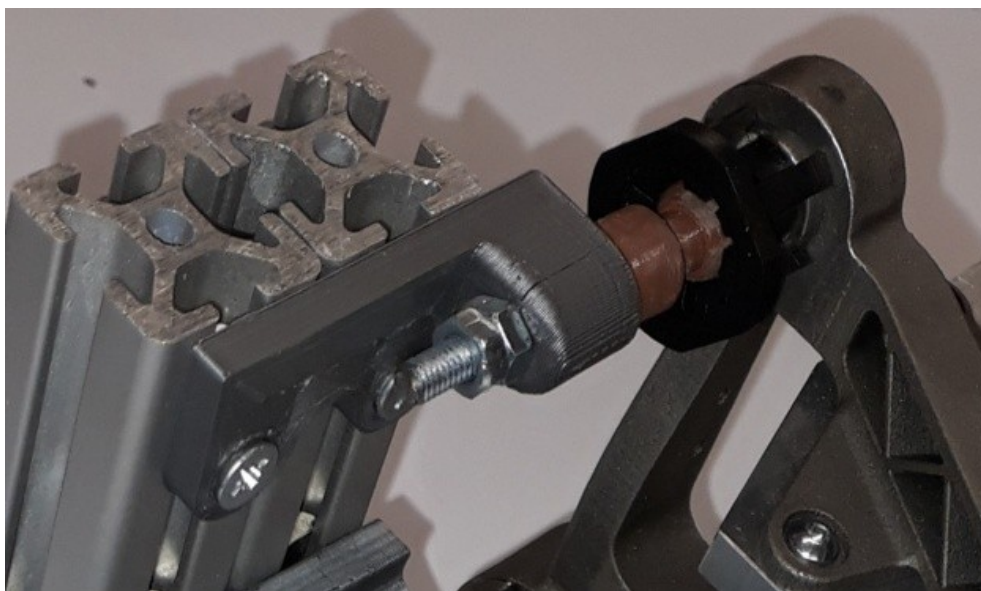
Sestava přípravku proti otáčení pístnice včetně všech komponent
